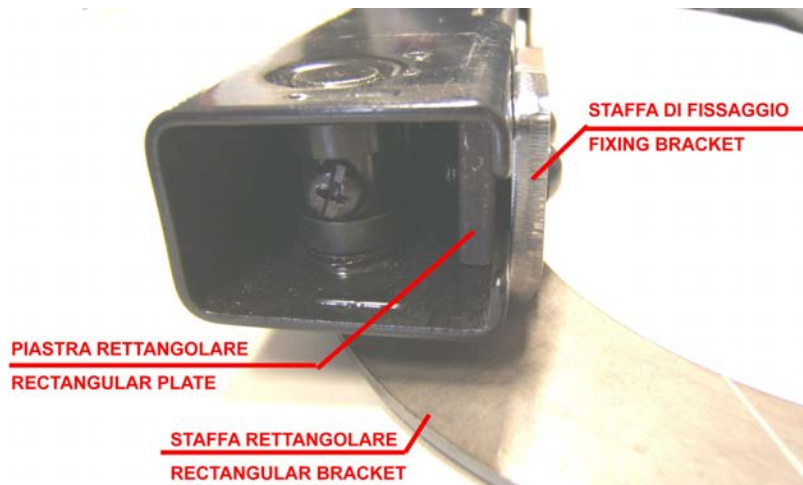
Montaggio della staffa con oliva sul chiudiporta - Assembly of the bracket with roller on the door-closer
